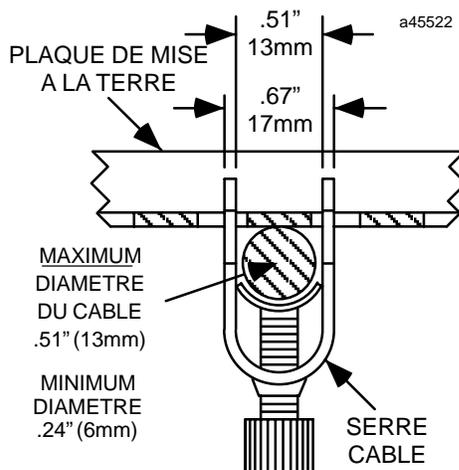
Vue en coupe d'un câble fixé par serre-câble
